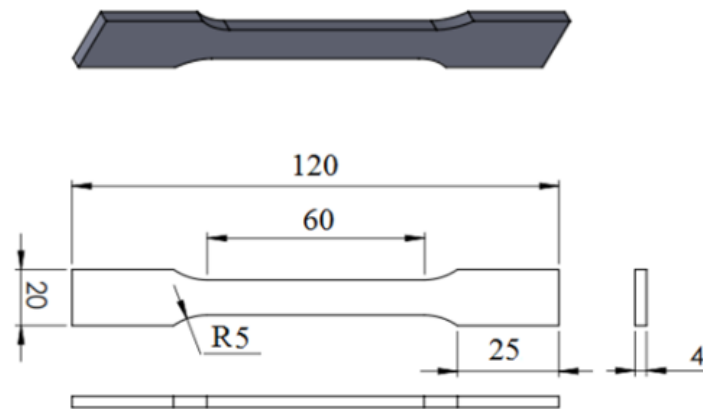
Géométries de l'éprouvette de traction non soudée [5]
